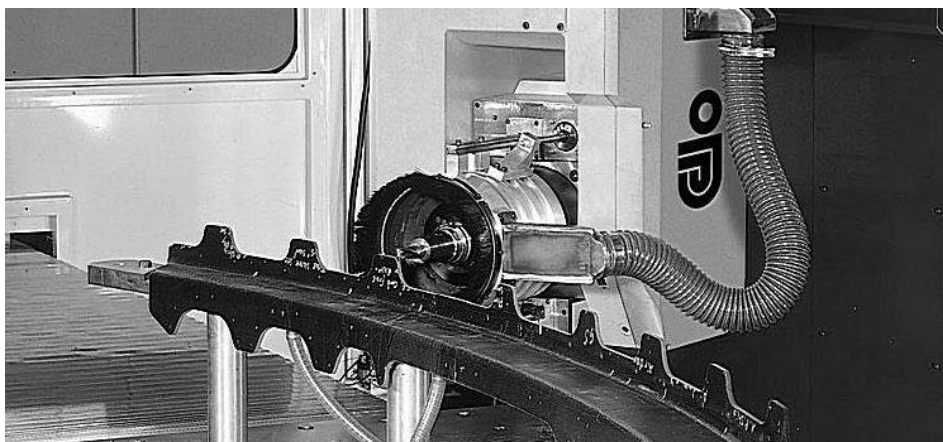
Приймальник-уловлювач на шпинделі фрезерного верстата
